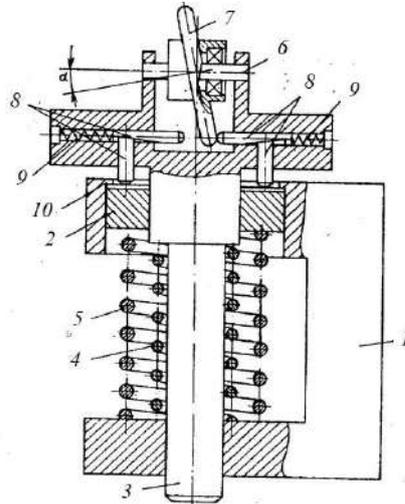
Конструкция для ППД галтелей (1- корпус; 2 – втулка; 3 – державки; 4,5 – пружины; 6 - ось; 7 – ролик; 8 – два клиновых передаточных механизма; 9 – пружины для передаточных механизмов; 10 – выступ)
